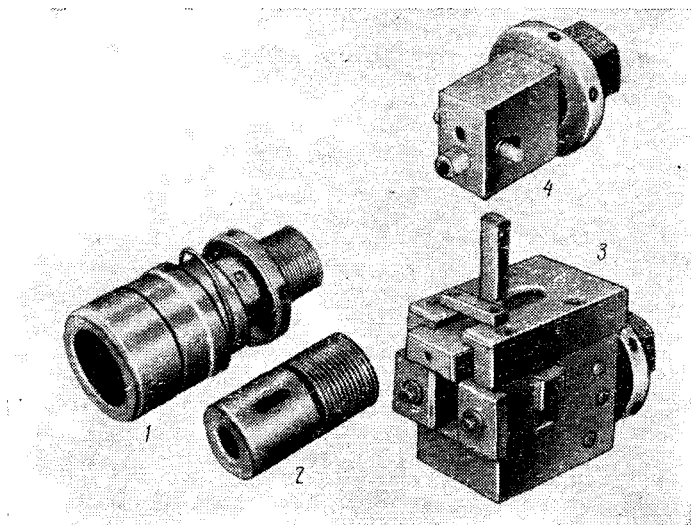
Патроны для закрепления протяжек с различными хвостовиками:
